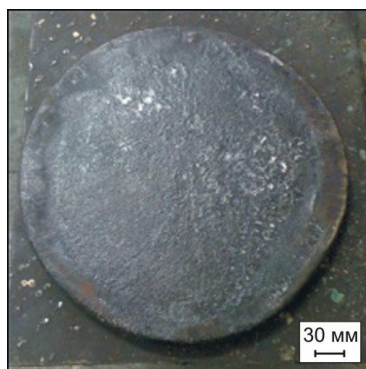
Внешний вид дисковой заготовки из опытного орто-сплава, полученной по упрощенной схеме изотермической деформации (без смены осей деформации)
